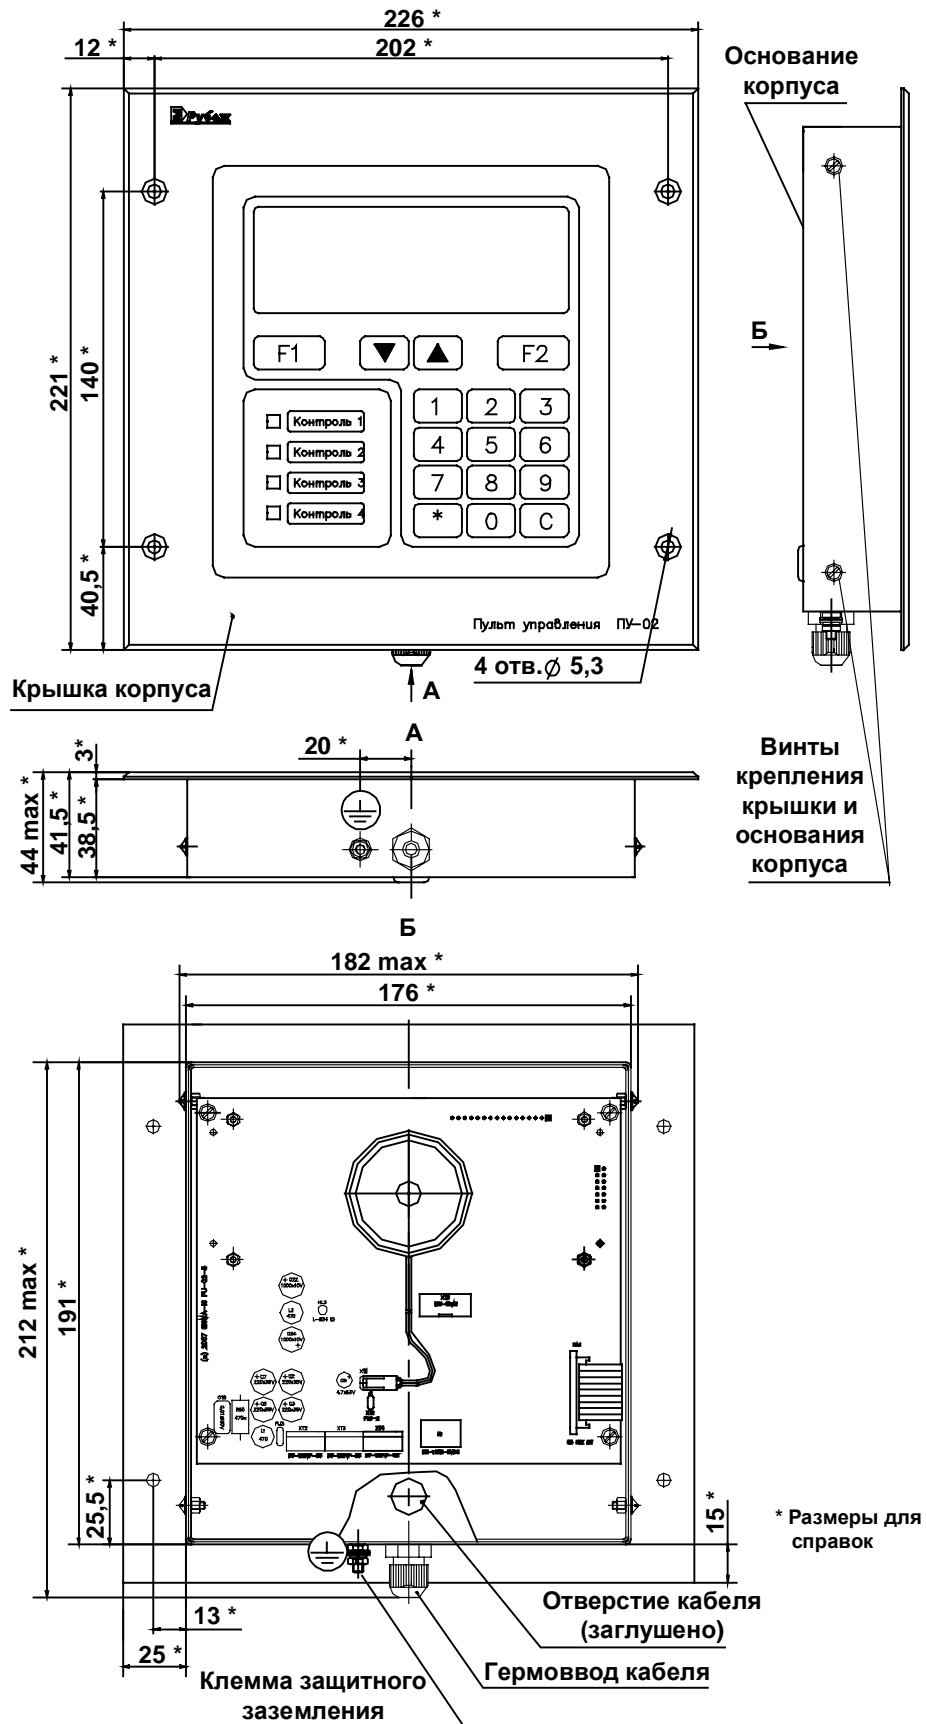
Габаритные и присоединительные размеры (врезное исполнение Тип 1)
